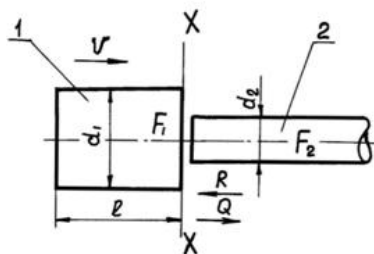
Розрахункова схема осевого зіткнення поршня і передньої головки пневмоударника П1-75: 1 – поршень; 2 – передня головка
